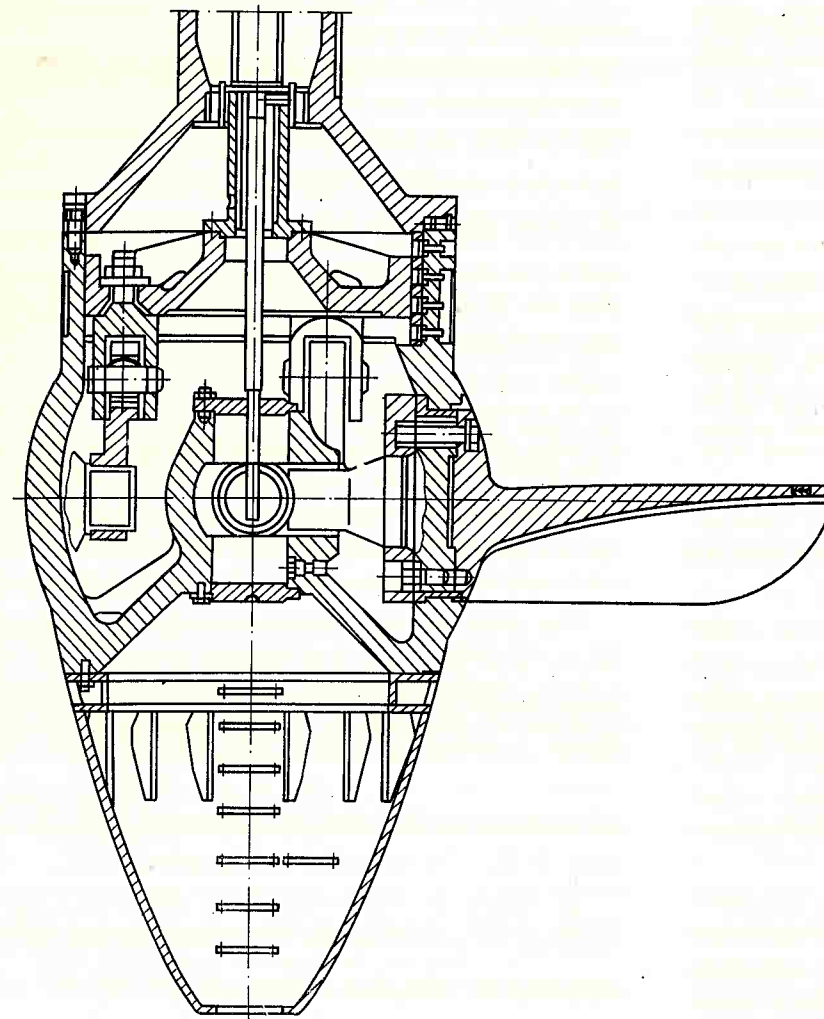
Разрез по рабочему колесу бескрестовинного типа с полостью сервомотора во втулке рабочего колеса поворотной-лопастной гидротурбины
